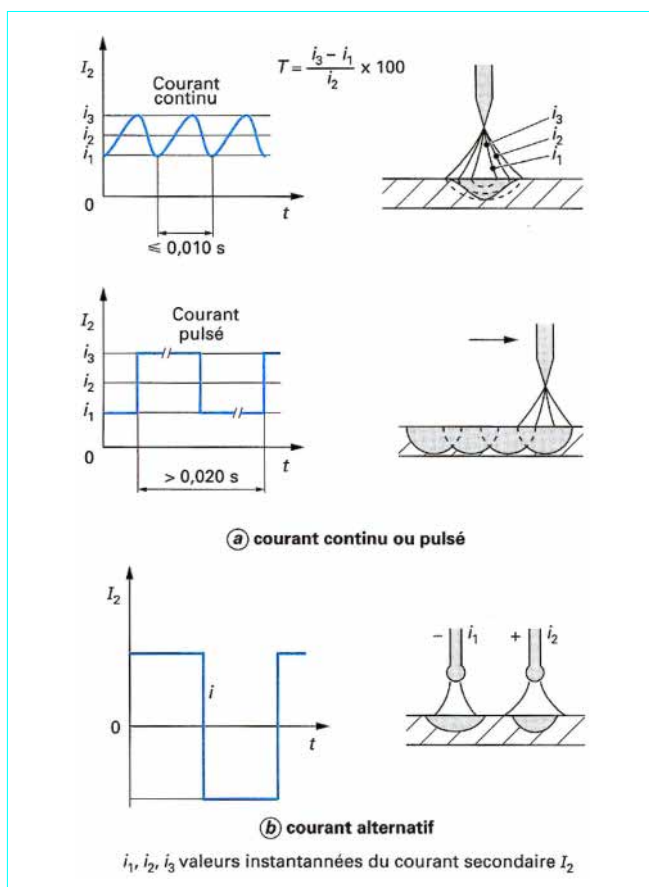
Effet du courant continu ou alternatif sur la soudure
